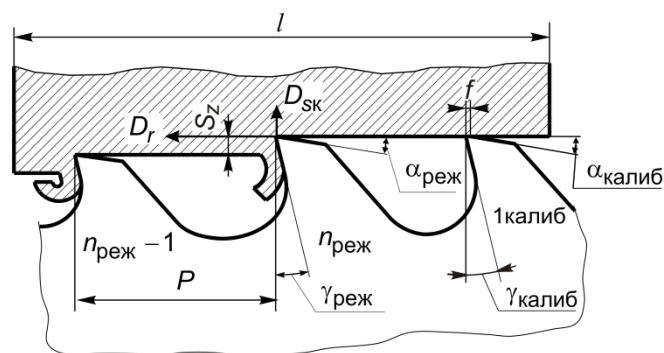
Схема срезания слоя материала зубьями протяжки; размеры и геометрические параметры режущих и калибрующих зубьев протяжки
